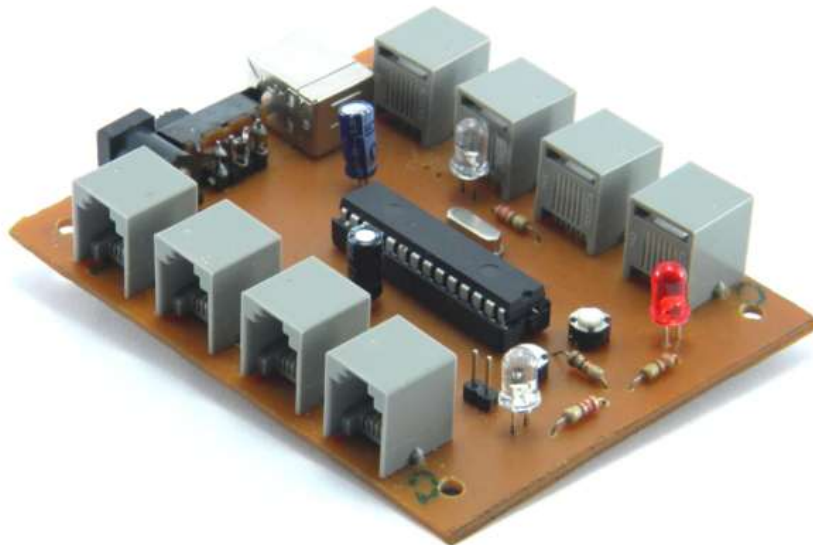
(g): PCB módulo de control terminado del AP
